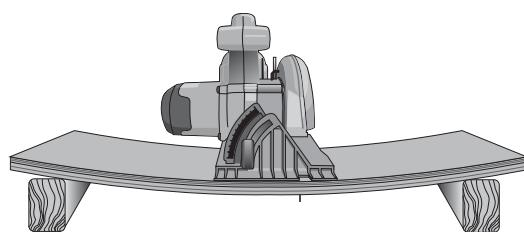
NE JAMAIS soutenir la planche ou le panneau LOIN DE la ligne de coupe.
